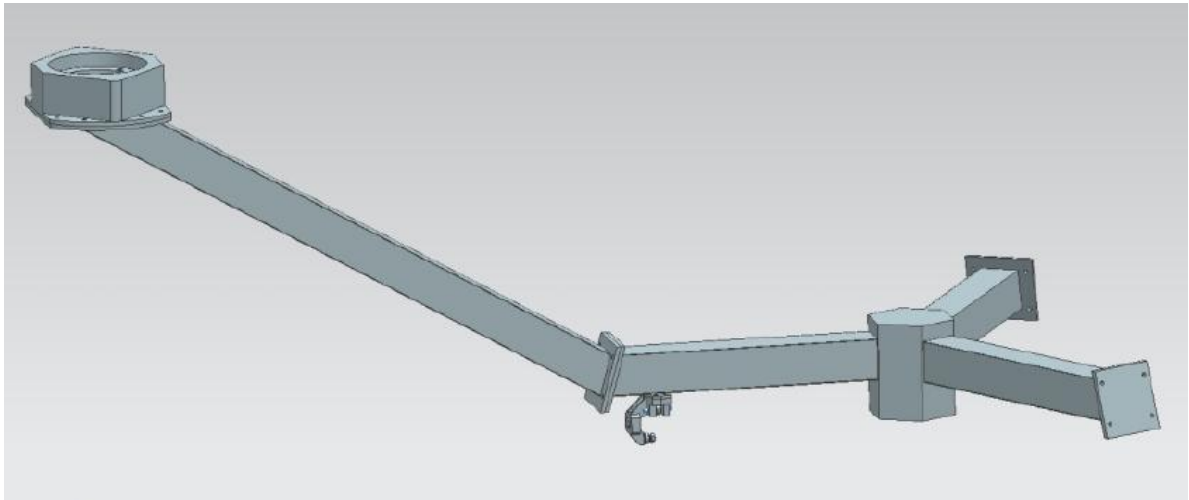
Soluzione di partenza: braccio a sezione rettangolare, collegamento fra il profilo e il rotore della turbina.
